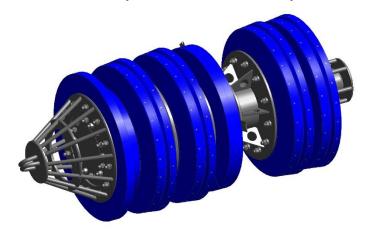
Общий вид поршня-разделителя ПРВ2
